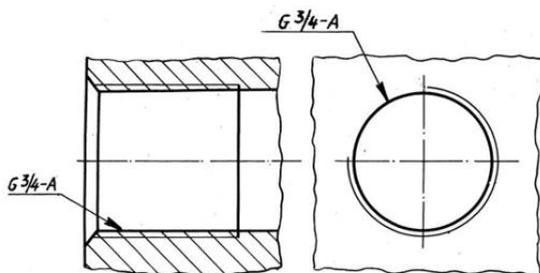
Обозначение внутренней цилиндрической трубной резьбы
